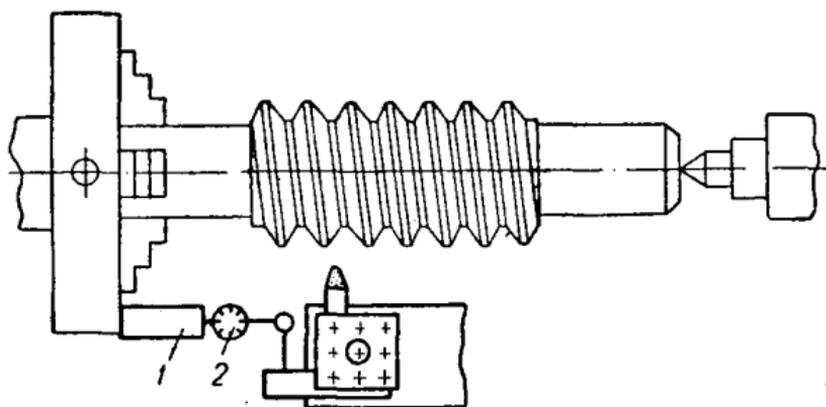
Схема деления заготовки при нарезании многозаходной резьбы по методу Г. Н. Смирнова.
